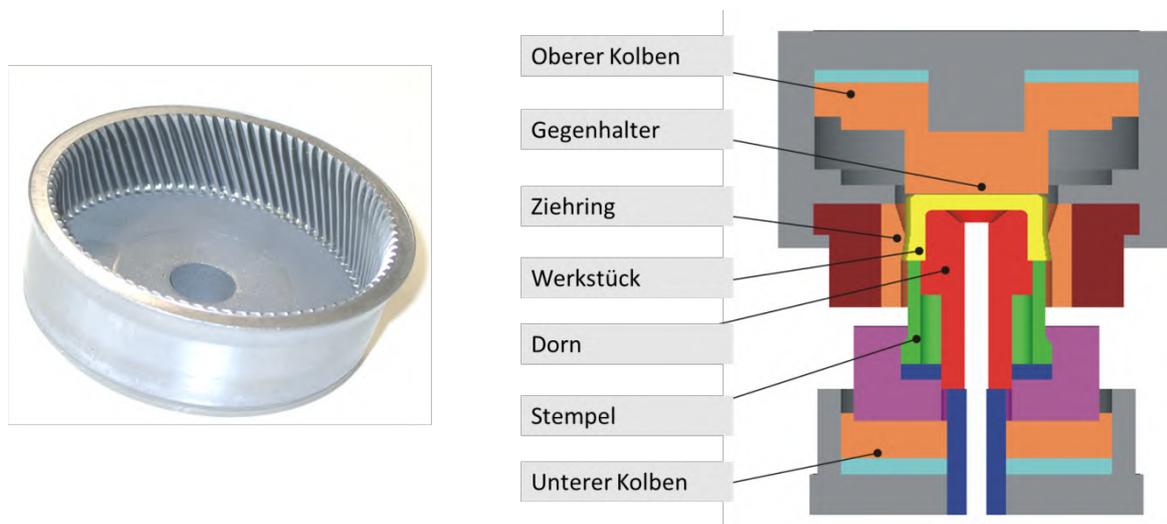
Fließpressen innen schräg verzahnter Hohlräder [10]
